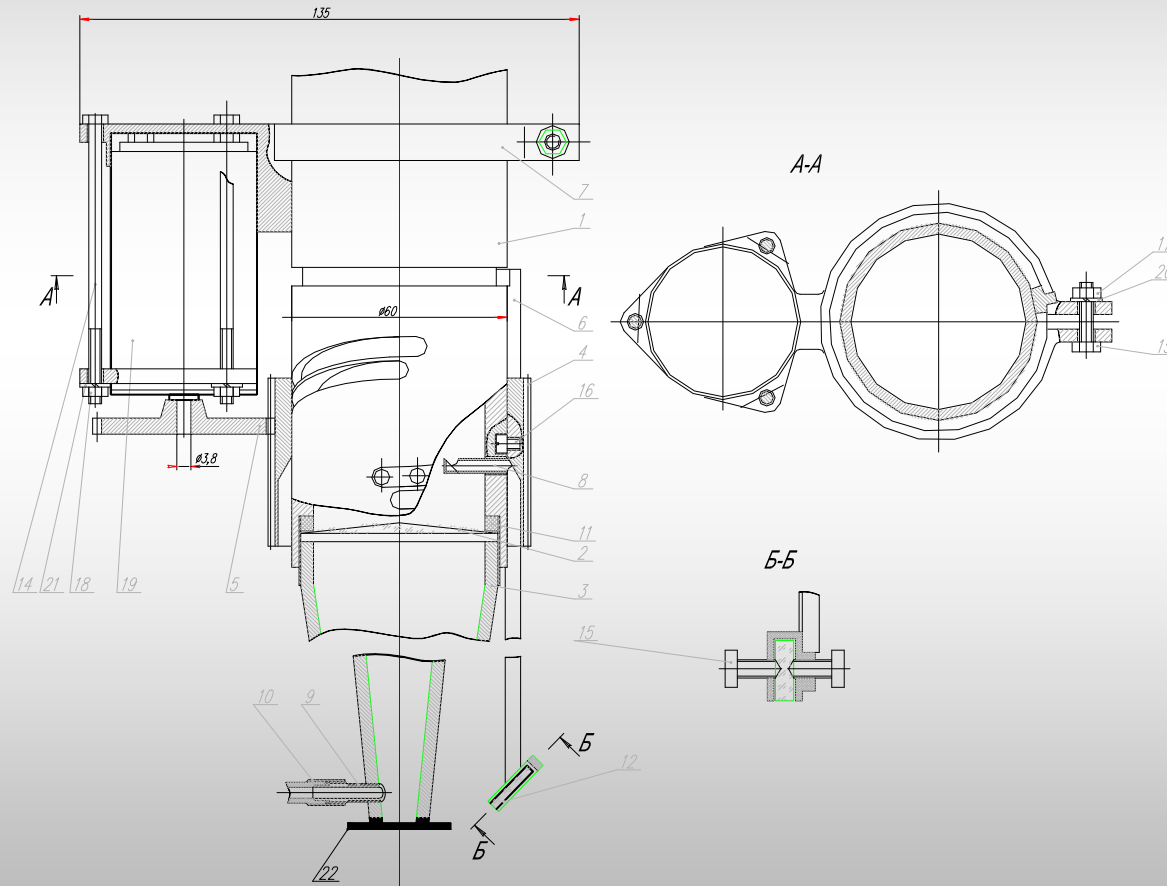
К. Конструкція різачка для контурної обробки з урахуванням дійсного рівня поглинання випромінювання зоною обробки
